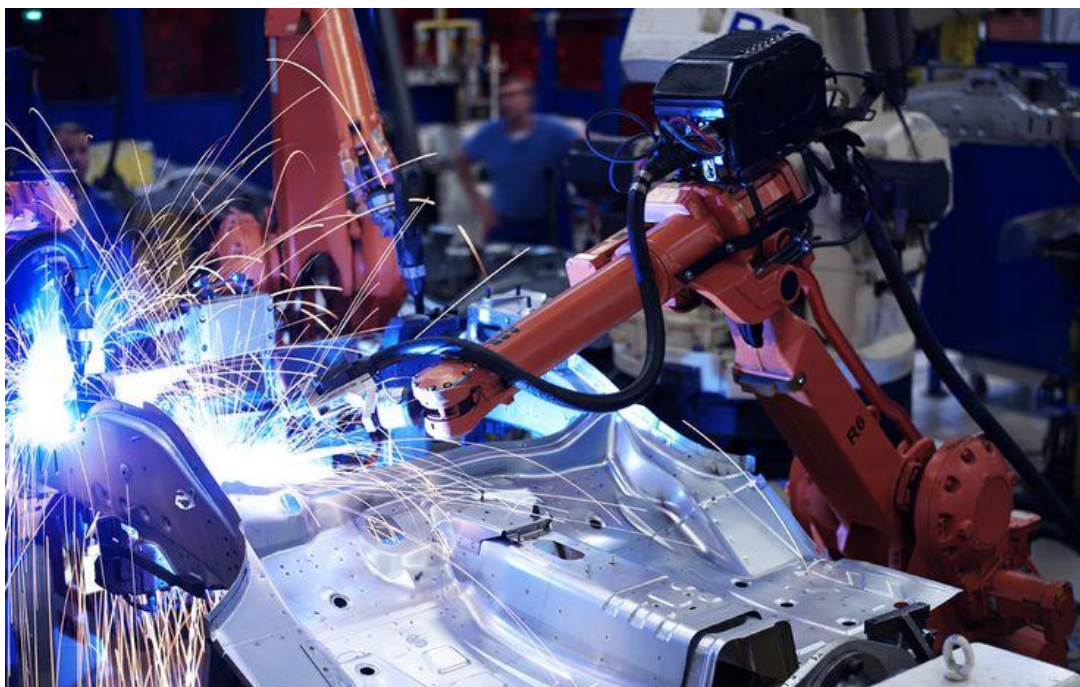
Robot de soldadura continua (MIG)
